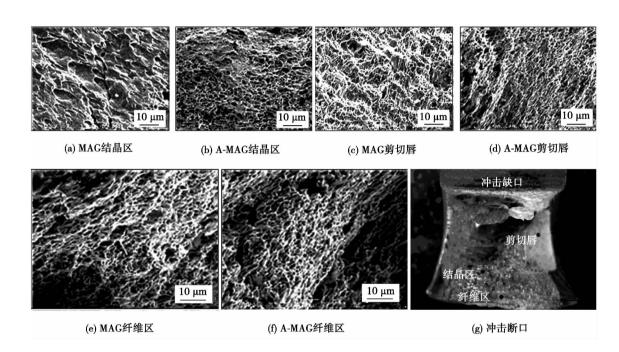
冲击断口形貌 Fig. 4 Impact fracture morphology
